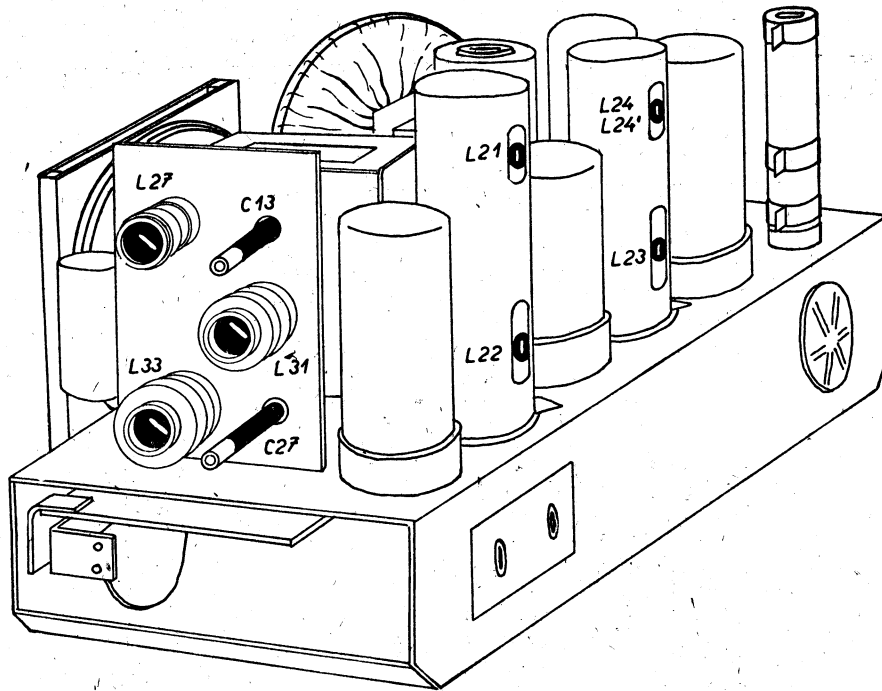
ZAPOJENÍ PŘIJIMAČE NA CHASSIS
